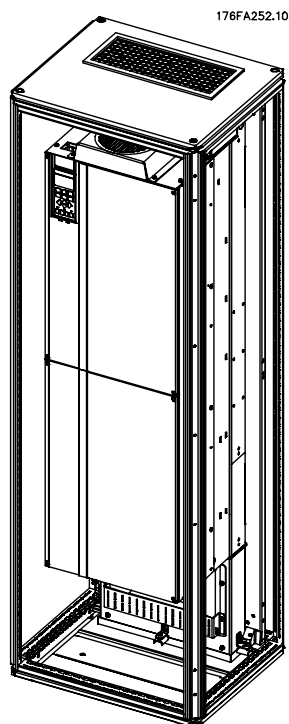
Installation du IP00 sur la protection Rittal TS8.
